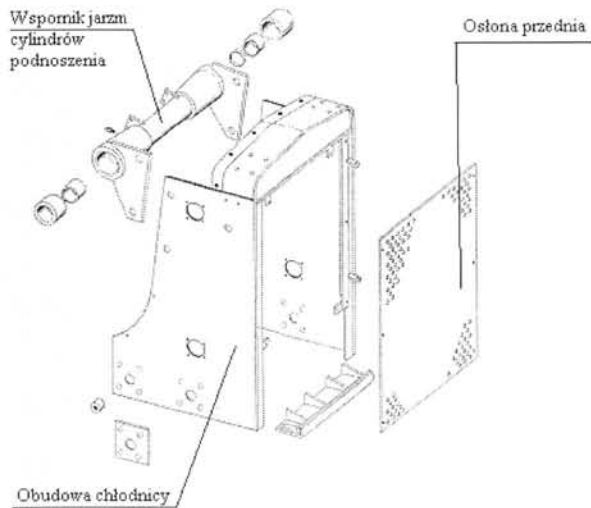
Przestrzenny schemat konstrukcyjny ramy przedniej z zaznaczonymi jej zasadniczymi elementami.
